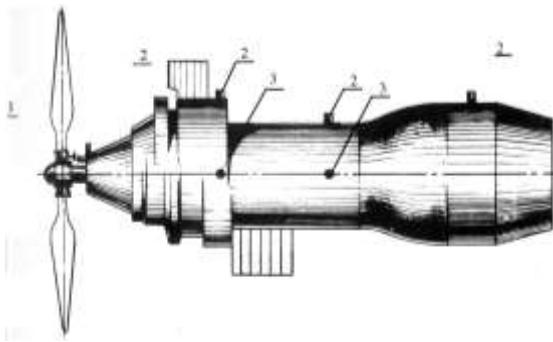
Препарировка ТВД для балансировки воздушного винта:
